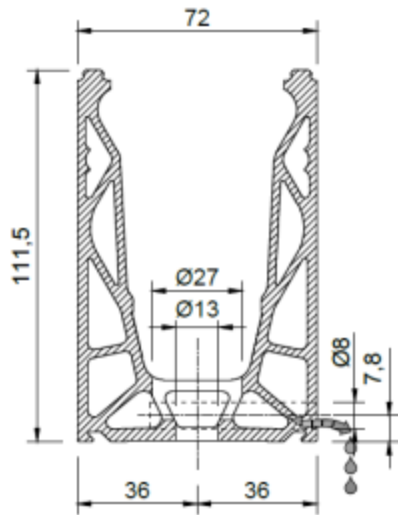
section transversale du profilé DF88LM.60 avec indication de perçage pour drainage
